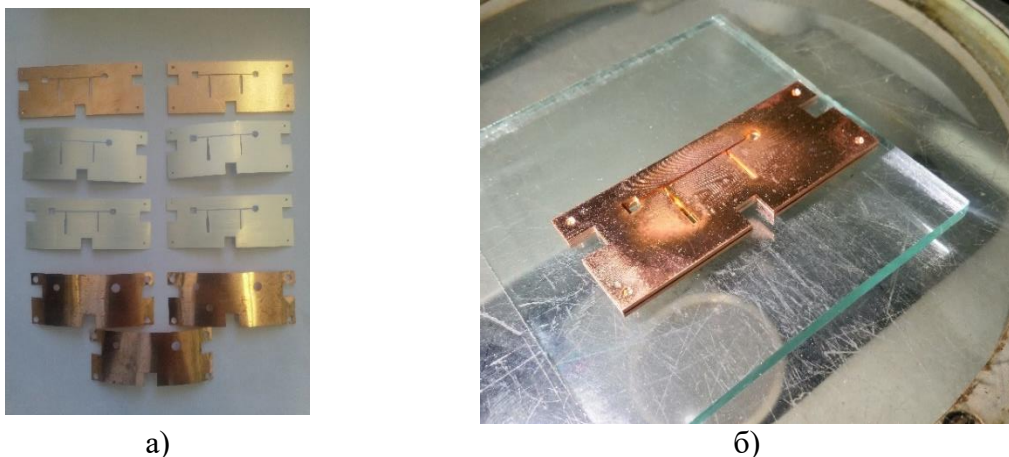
а) набор пластин для сборки пакета б) пакет после пайки
